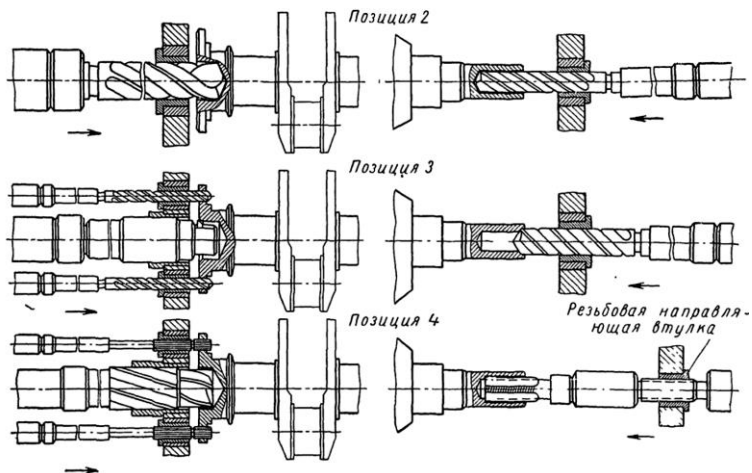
Эскиз наладки двустороннего сверлильного агрегатного станка с четырехпозиционным барабанным приспособлением для обработки отверстий в переднем и заднем концах коленчатого вала
